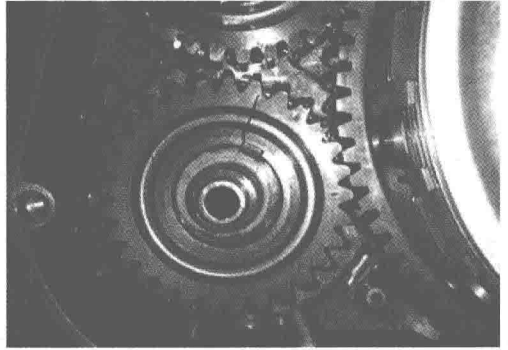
齿轮的疲劳裂纹^[8]
